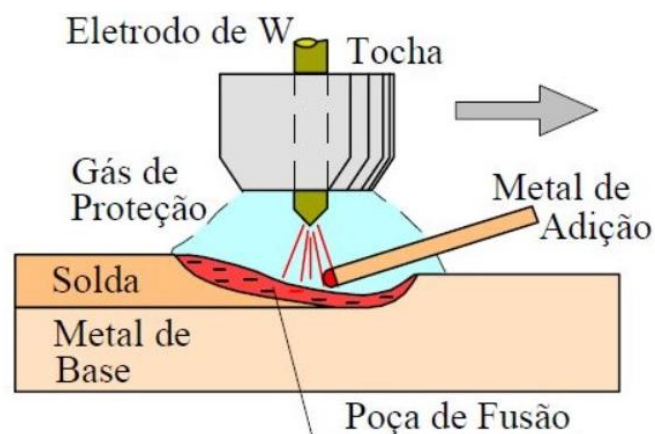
Equipamento utilizado e demonstração da soldagem GTAW [8].
